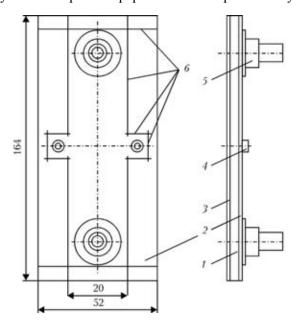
Схема измерительной камеры магнитопневматического газоанализатора типа ОХҮМАТ: 1 — основание; 2 — верхняя пластина; 3 — нижняя пластина; 4 — ниппель; 5 — штенгель; 6 — нахлесточные сварные швы
